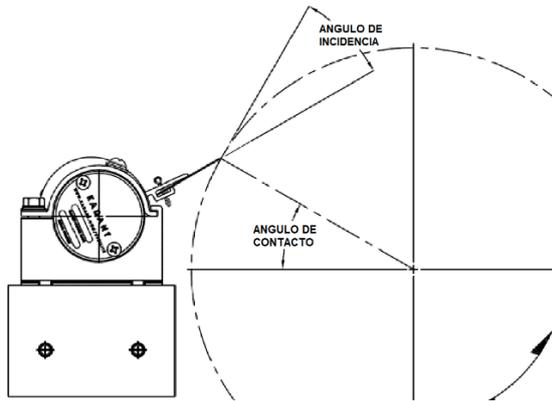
Dispositivo mecánico con lámina de ataque para limpieza del rodillo.
